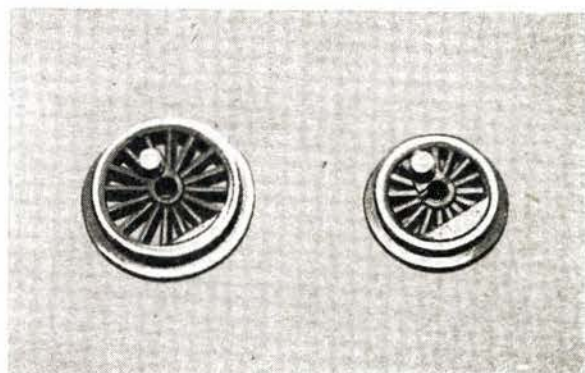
H0-Laufradkranz auf 9,0 mm Innendurchmesser ausgedreht.
